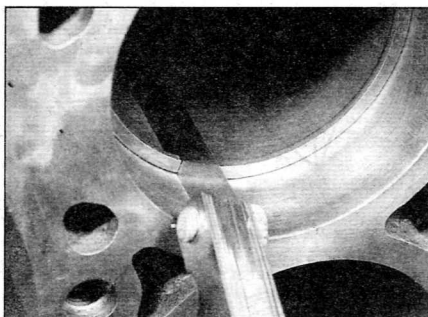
Измерьте зазоры в стыках поршневых колец с помощью «веерного» щупа
